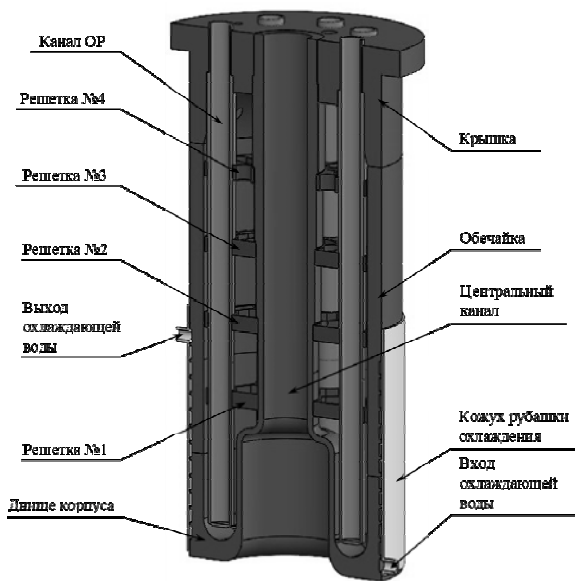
Конструктивная схема корпуса АЗ перспективного ИЯР ВИР-3
